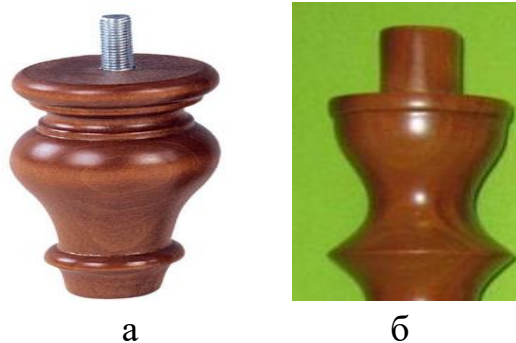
Образцы опор для мягкой мебели: а – с металлической шпилькой; б – с круглым цилиндрическим шипом
